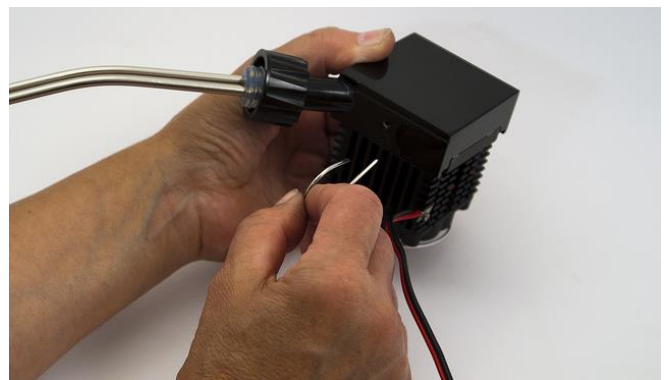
El dedo de enfriamiento Peltier necesita ser cerrado utilizando una pinza de cierre.
